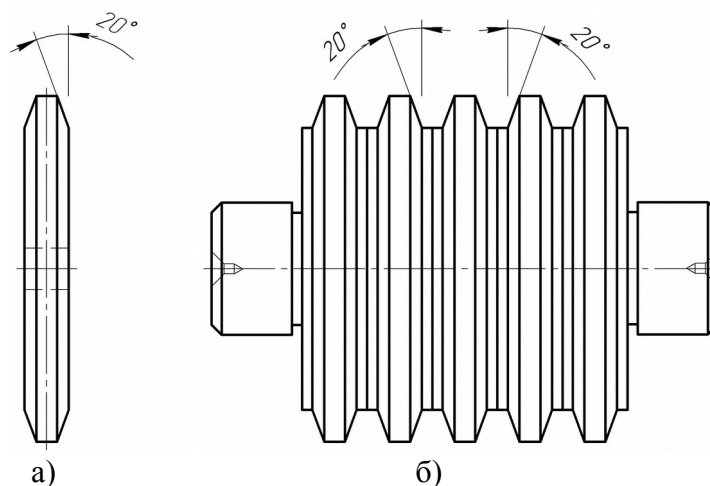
Накатники для формирования червячной поверхности гиперboloидного шлифовального круга: а) прямобочный ролик; б) каскад прямобочных роликов
